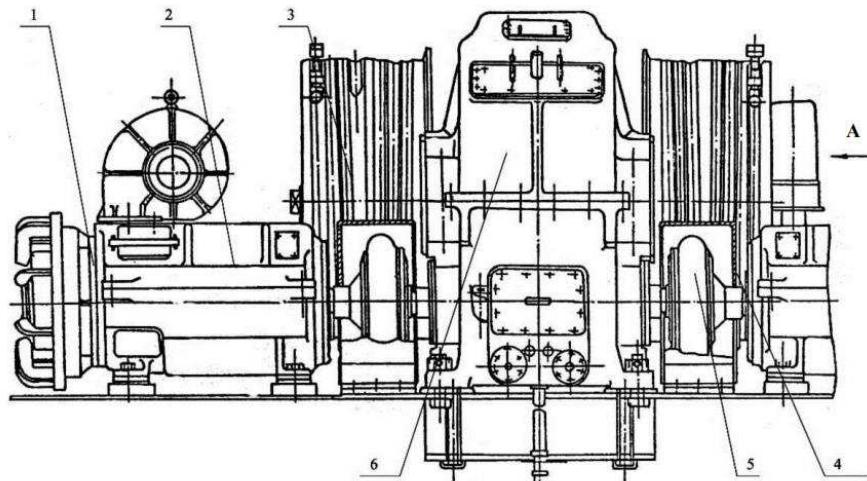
Лебедка напора (вид спереди)
